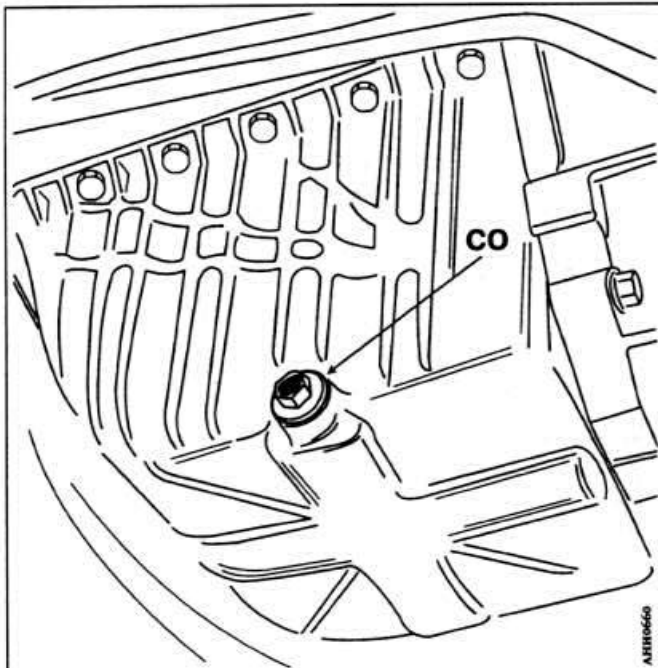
Расположение пробки сливного отверстия масляного картера двигателя. CO — сливное отверстие
